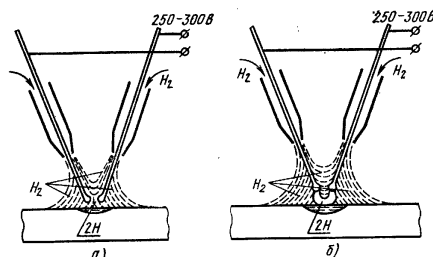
Схема процесса атомно-водородной сварки:
